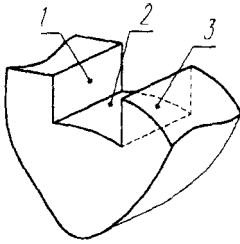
Схема расположения формируемых поверхностей на заготовке
